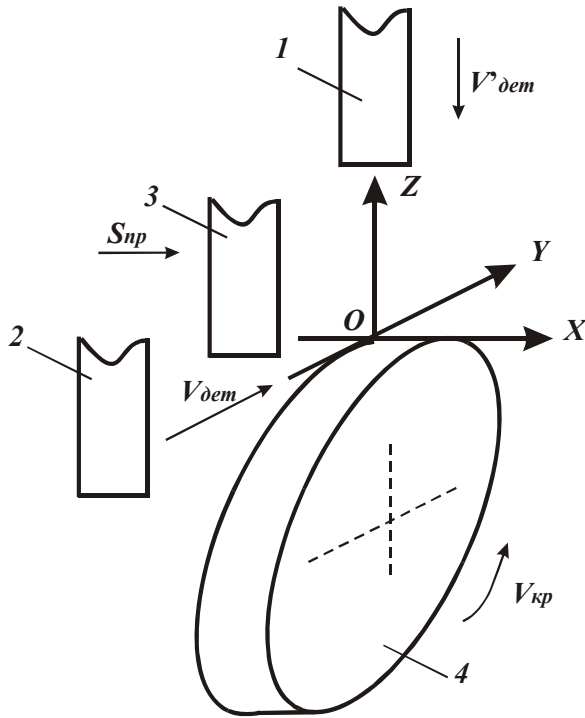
Три принципиальные схемы формирования шероховатости поверхности при шлифовании: 1, 2, 3 – положения обрабатываемого образца, 4 – шлифовальный круг.
